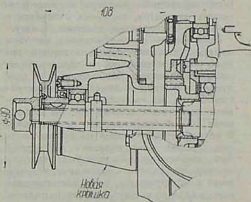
Насадка шкива привода воздушодувки на коленчатый вал двигателя М-72.
